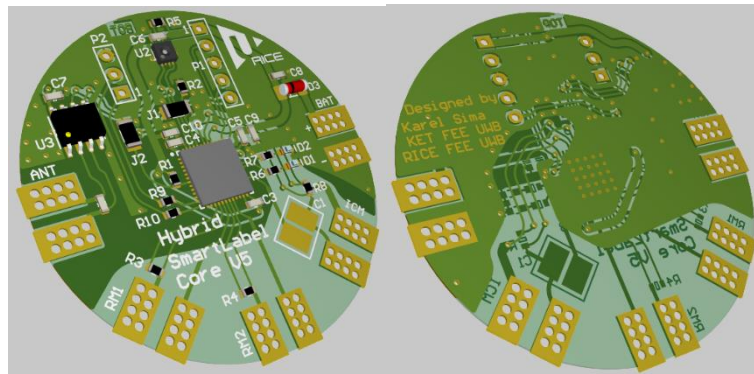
Sesazení grafického souboru PCB a návrh tištěného motivu v CAD
